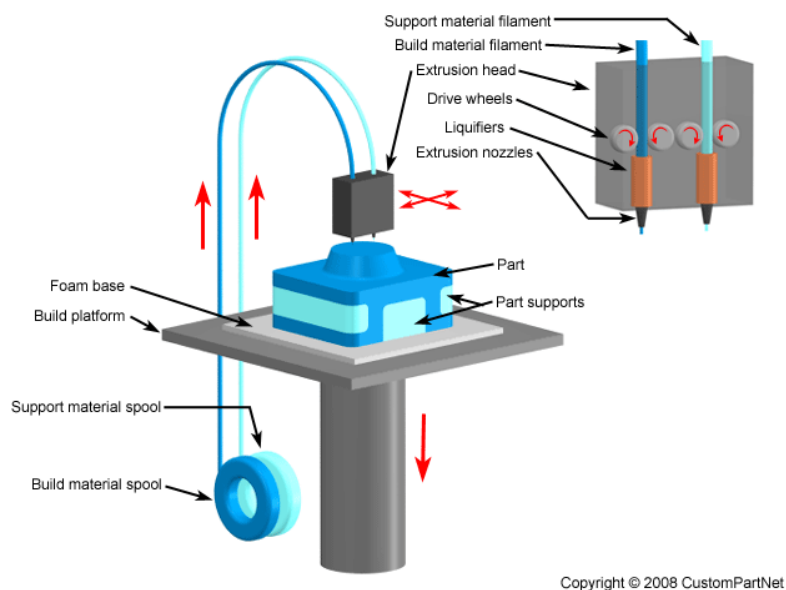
Tecnica di stampa Fused Filament Fabrication (FFF)
